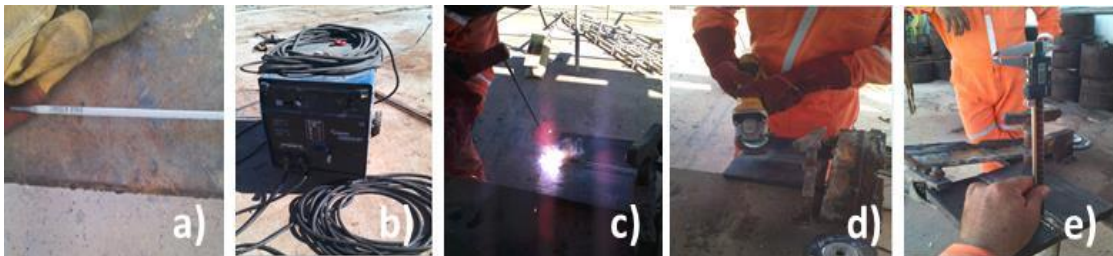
Realización de actividades: a) Material de aporte, b) Máquina de soldar, c) Aplicación del material de aporte, d) Limpieza de la soldadura, e) Medición de corona del cordón nuevo
